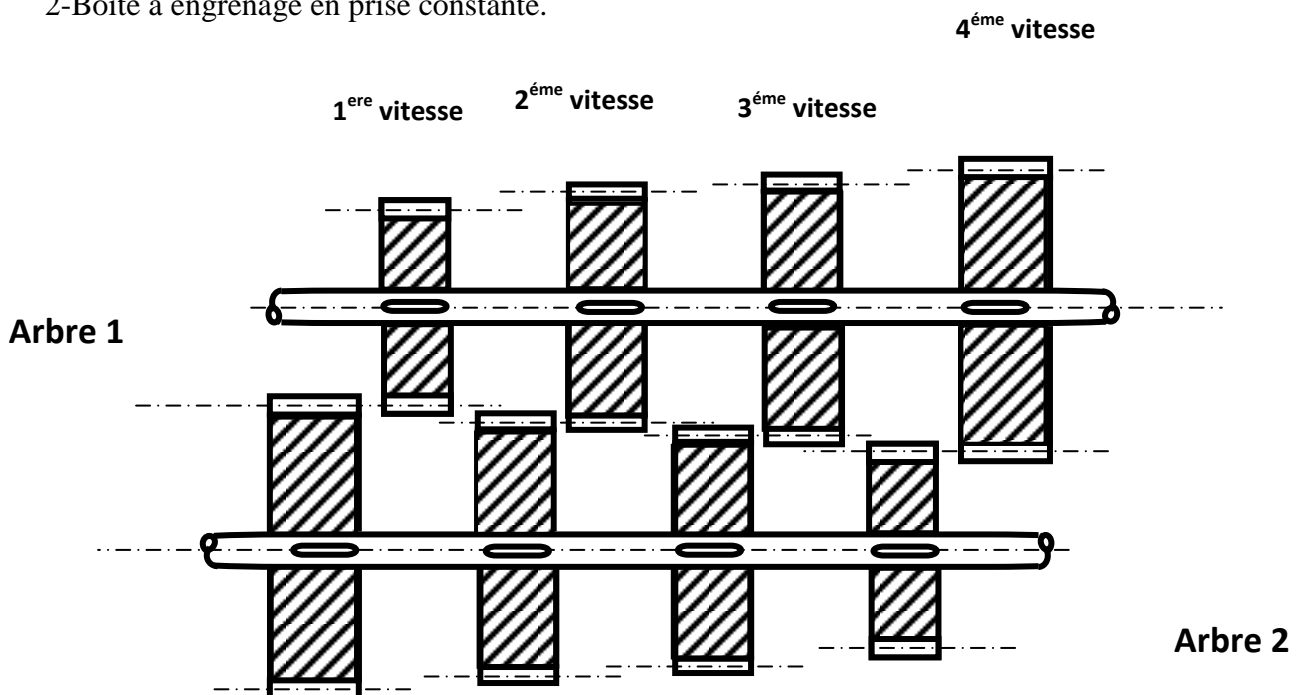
Boîte vitesse à engrenage en prise constante
